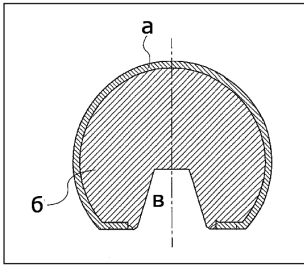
Поперечний переріз ендопротеза головки стегнової кістки: а) металева оболонка; б) полімерна серцевина; в) конусний отвір
